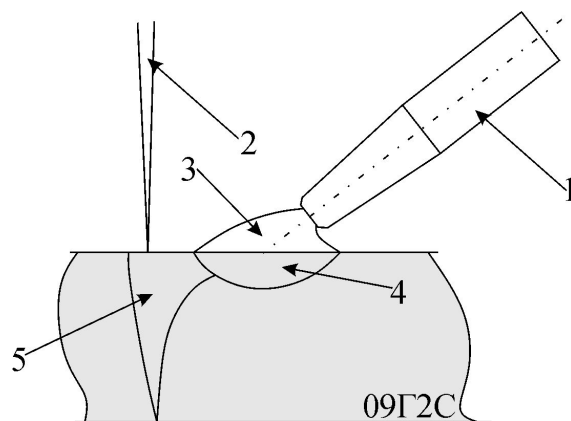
Схема процесса гибридной лазерной сварки
